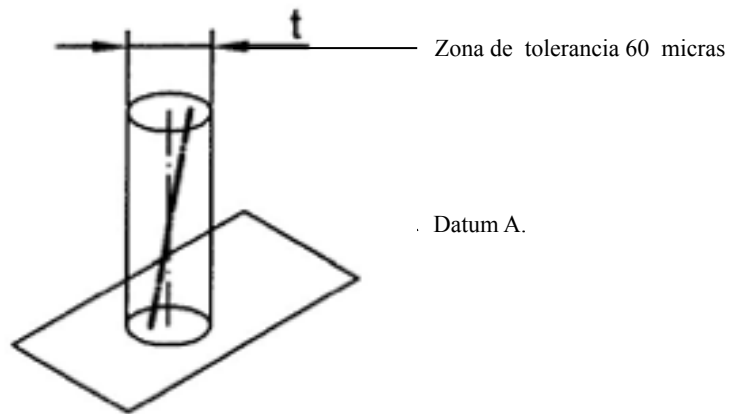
Zona de tolerancia para la perpendicularidad referenciada sobre el Datum A.
